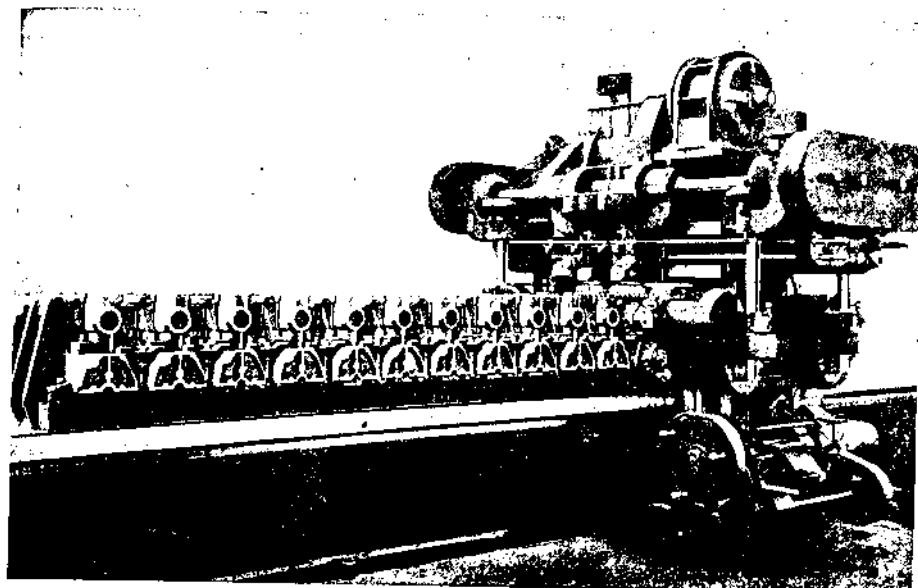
Специальный продольно-фрезерный станок Ингерсоль.
